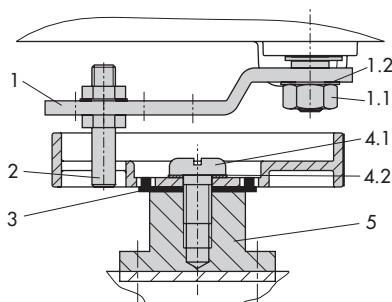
Montaje de la rueda de acoplamiento en el Tipo 3278
